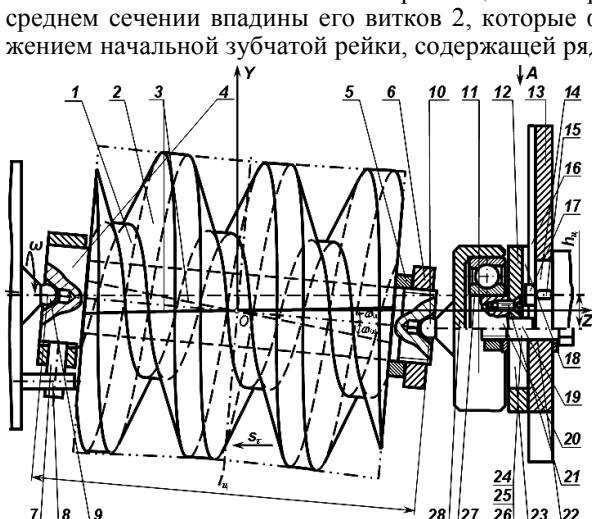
Схема установки гиперboloидного червяка на оправку со смещением заднего центра бабки станка и устройство для его осуществления
